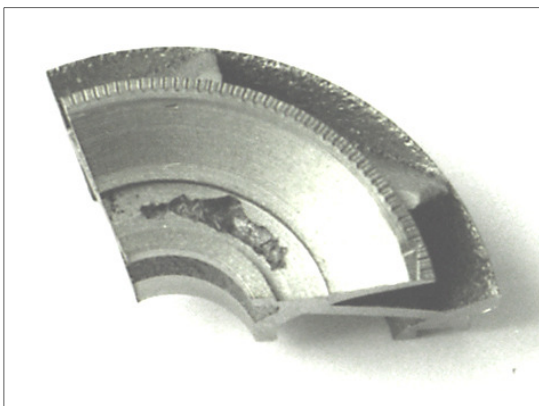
Фрагмент отливки «Рабочего органа» с окисленной шероховатой раковинной
